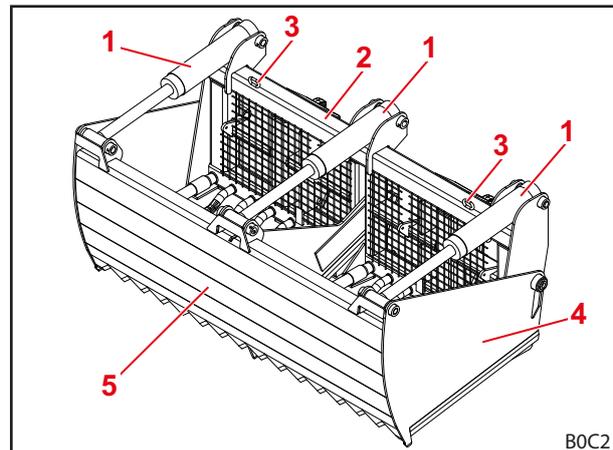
Aufbau Silageschneidzange mit 3 Hydraulikzylindern
